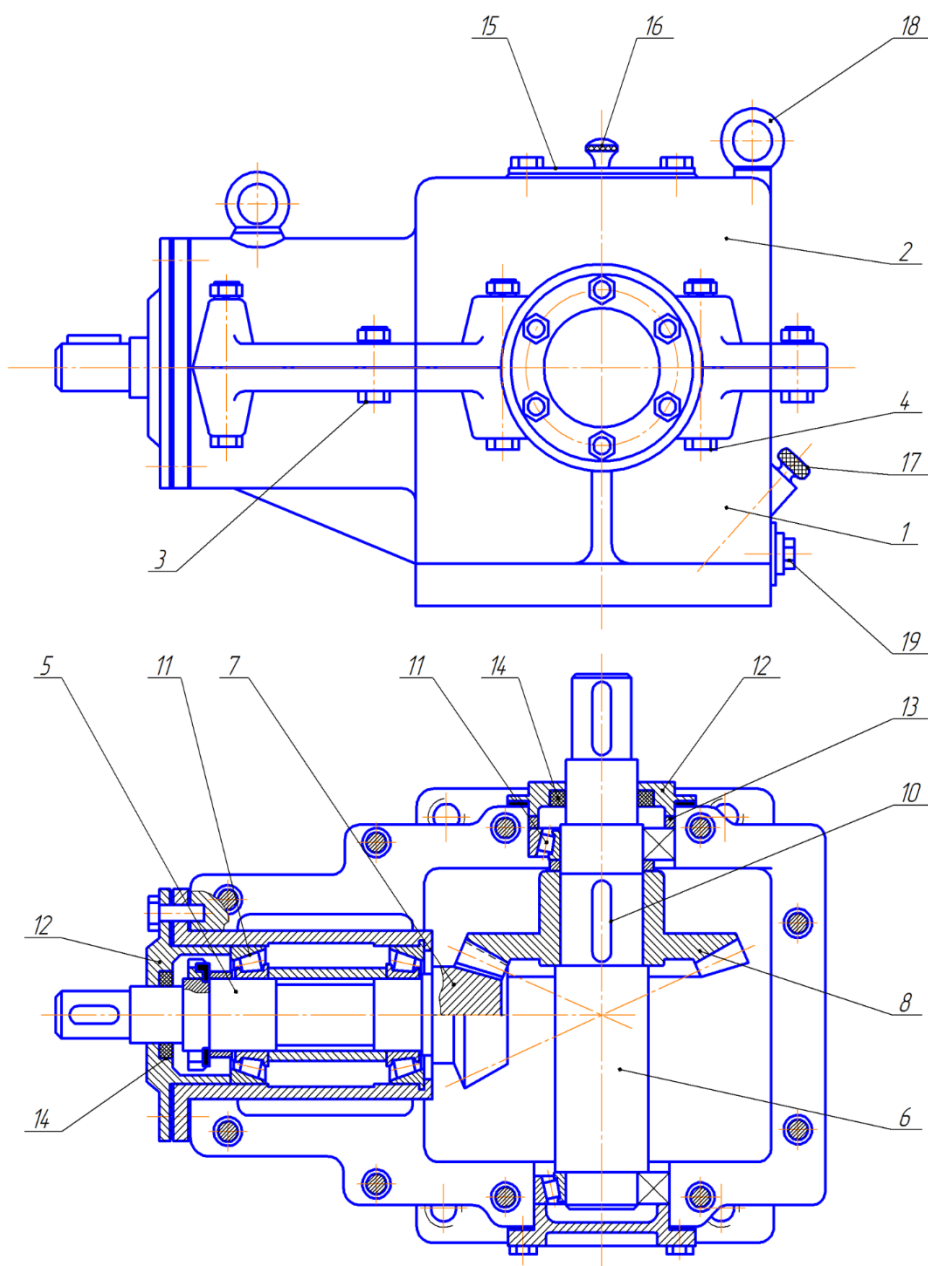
Конструкція одноступінчатого конічного редуктора
